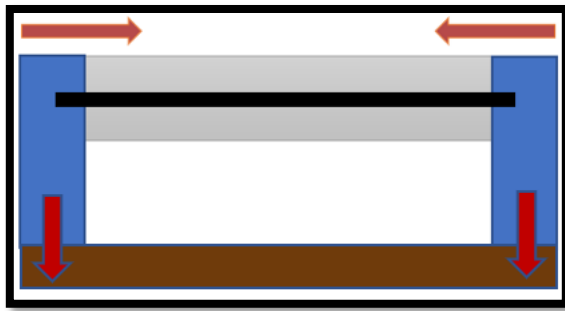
Esquema de l'estructura de la CNC vist de perfil. Font. Elaboració pròpia.
